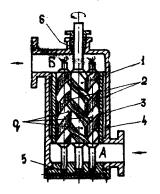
Схема устройства винтового насоса положении. Винты стальные и имеют двухзаходную винтовую нароку, образующую выступы и впадины. Ниже торцевые части интов выполнены в виде поршеньков и фиксируются в подпятнике 5. Ведущий и ведомые винты установлены с небольшим рациальным зазором в обойму 3. Обойма охватывает винты
